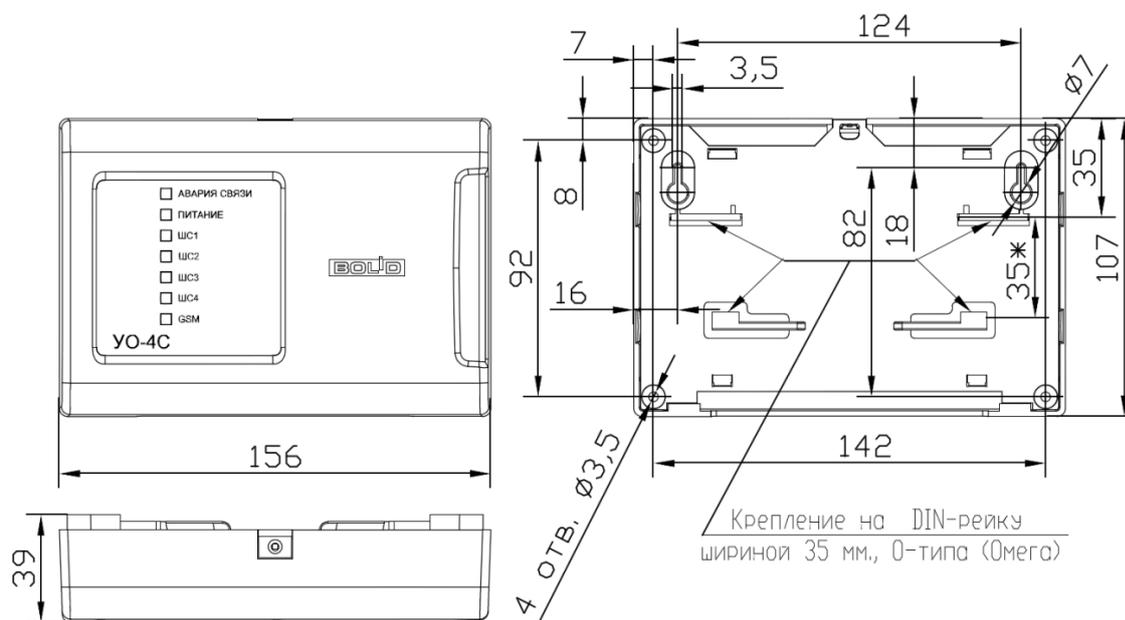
Габаритные и установочные размеры корпуса ПОО «УО-4С»
